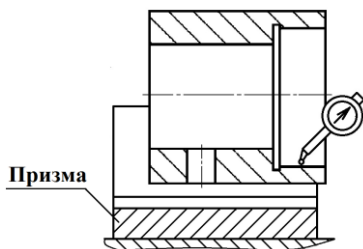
Схема измерения биения базовой и наружной цилиндрической поверхностей заготовки
